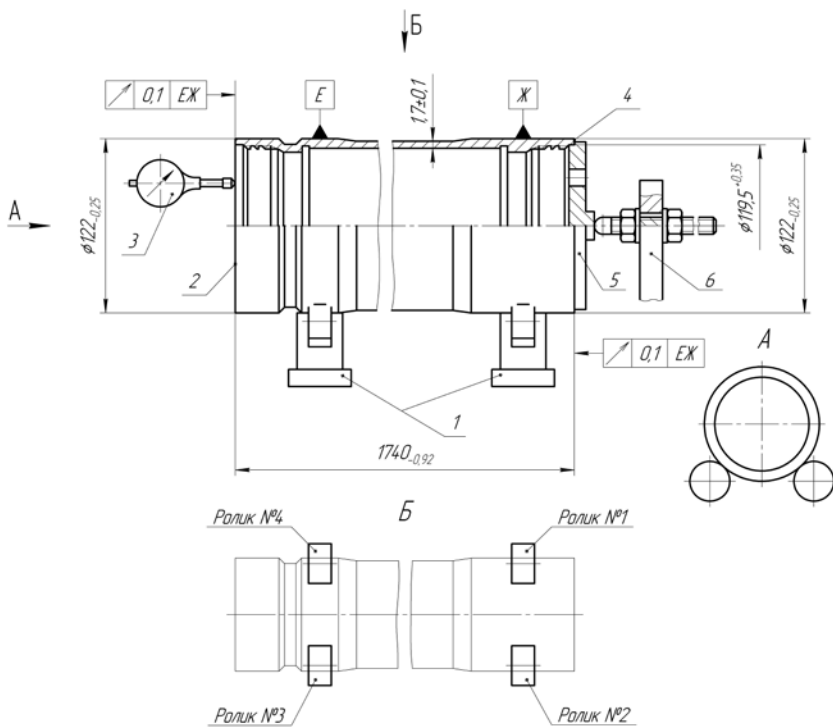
Схема контроля биения торцов базовой детали: 1 – роликовые призмы; 2 – торец № 1; 3 – индикатор часового типа; 4 – торец № 2; 5 – заглушка; 6 – упор
